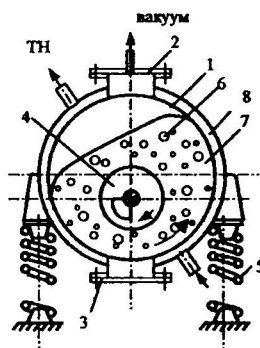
Вибро-вакуумная сушилка-мельница: 1- корпус; 2, 3- крышка загрузочного и выгрузочного люков; 4- вибратор; 5- упругая опора; 6- мелющие тела; 7- обрабатываемый материал; 8- теплообменная рубашка.
